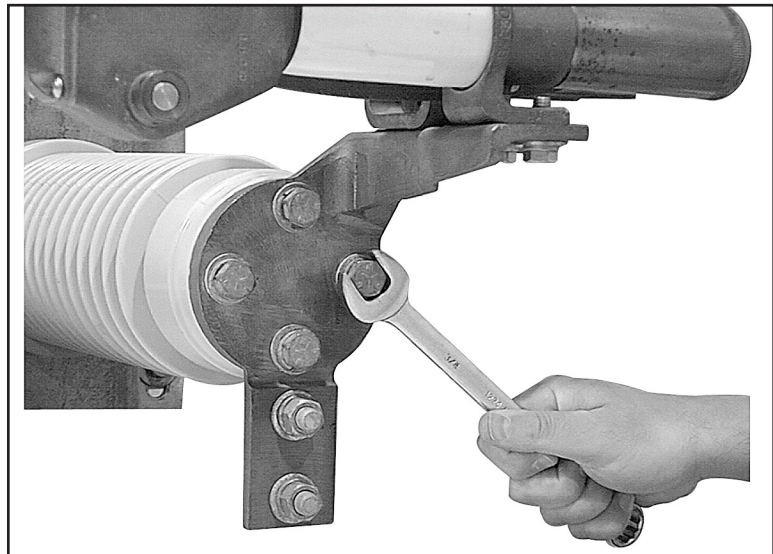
Desmontaje de la pieza fundida de la base terminal.
